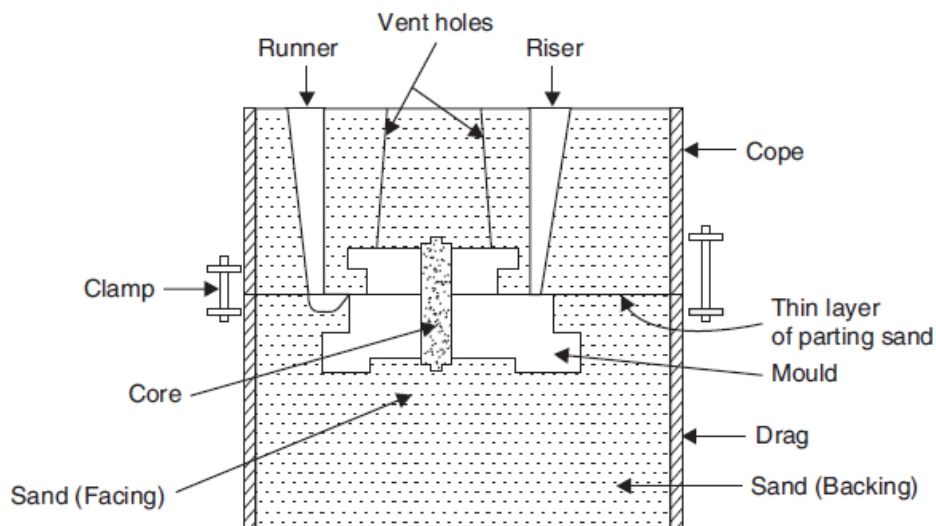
Esquema del molde para fabricar una pieza por fundición. H. N. Gupta, Manufacturing Processes, 2009.
